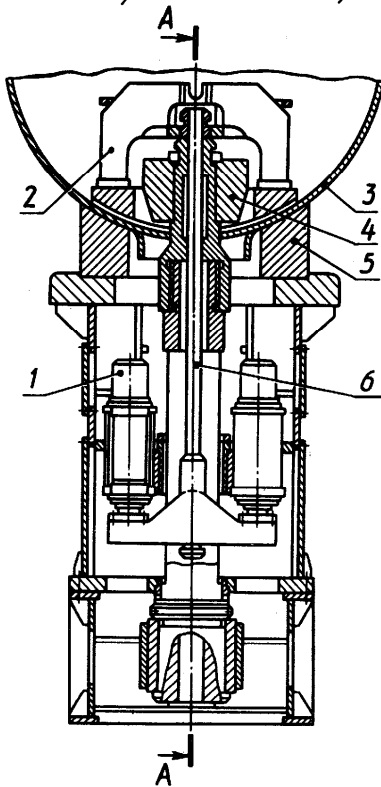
Пресс для отбортовки отверстий в корпусах аппаратов
